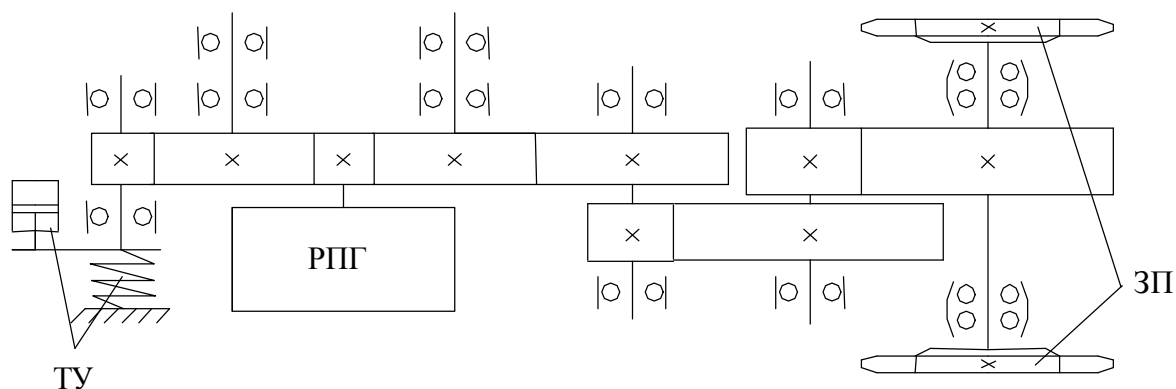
Кинематическая схема редуктора ходовой тележки комбайна
